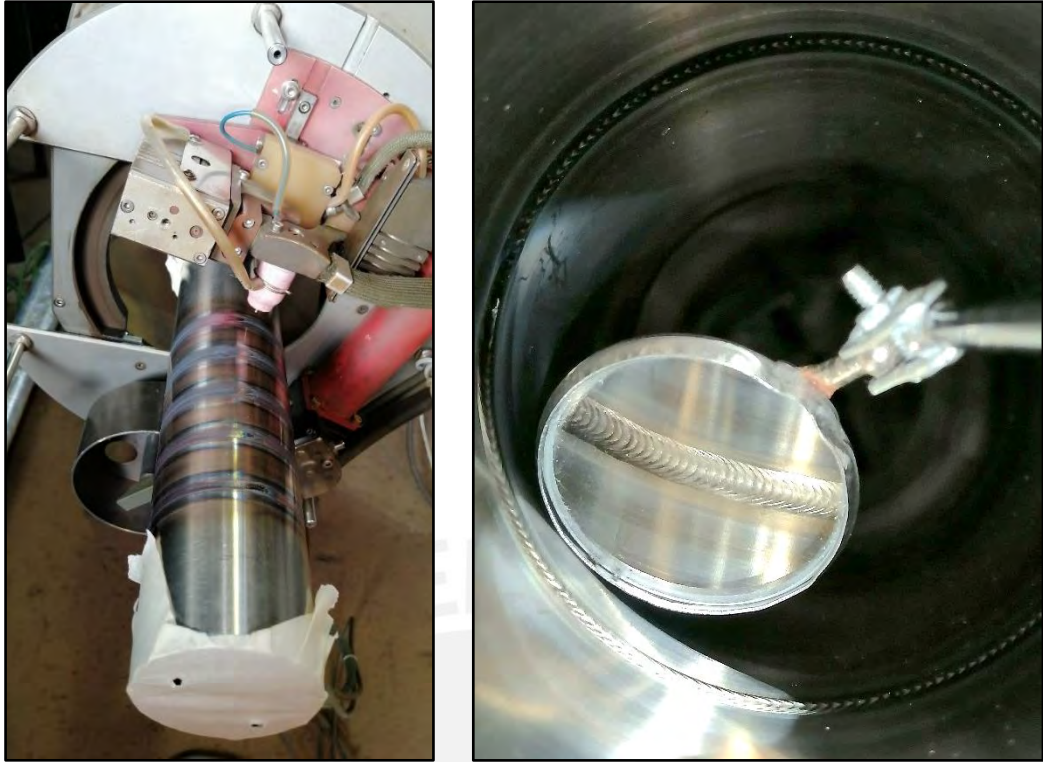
Inspección visual de líneas de fusión en el lado de la cara y raíz de la probeta luego de ejecutada la soldadura con los parámetros indicados en la Tabla 16
